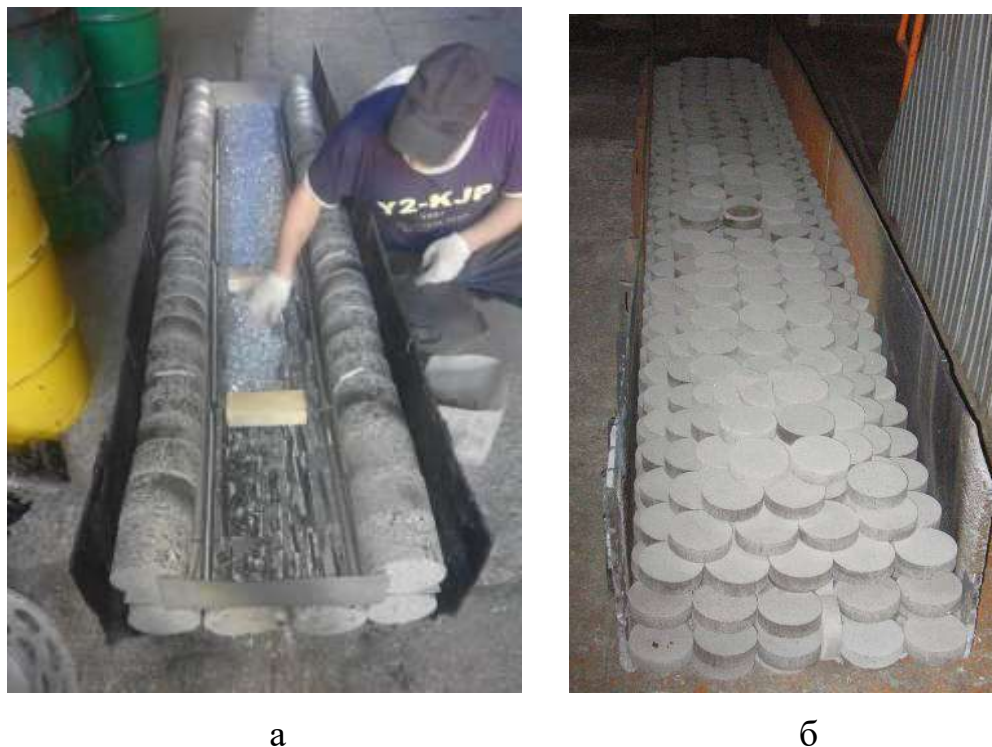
Шихтові заготовки для виплавки зливків титанових сплавів: а – VT22; б - VT23
